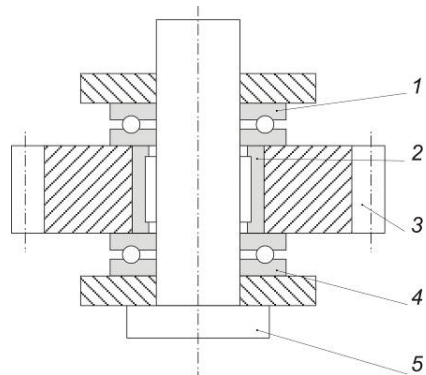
Схема приспособления для обкатки зубчатых колес
